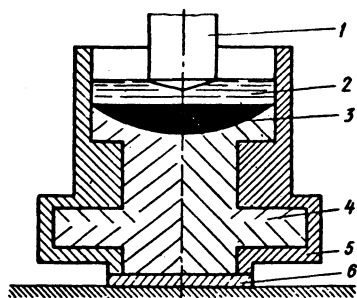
Схема ЭШП с прямым наплавлением металла в форму: 1 - расходуемый электрод; 2 - слой жидкого шлака; 3 - ванна жидкого металла; 4 - отливка; 5 - форма; 6 - поддон
